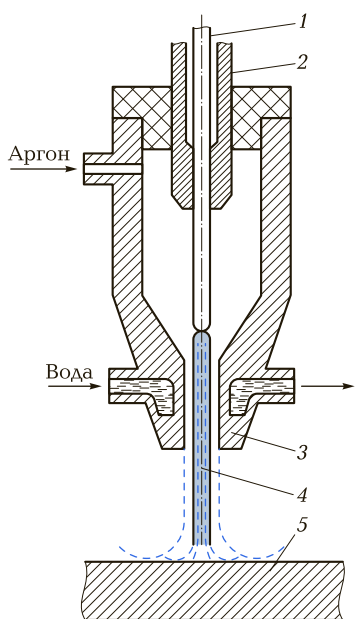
Схема процесса плазменной сварки:
